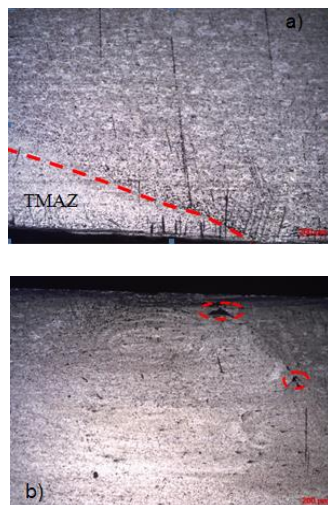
Soldadura da amostra FSW S1: a) Zona termo-mecanicamente afetada. b) Cordão de Soldadura.
